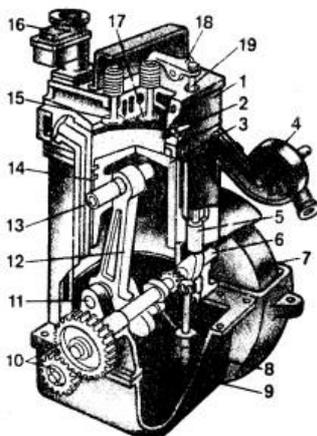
Устройство одноцилиндрового четырехтактного карбюраторного двигателя:
